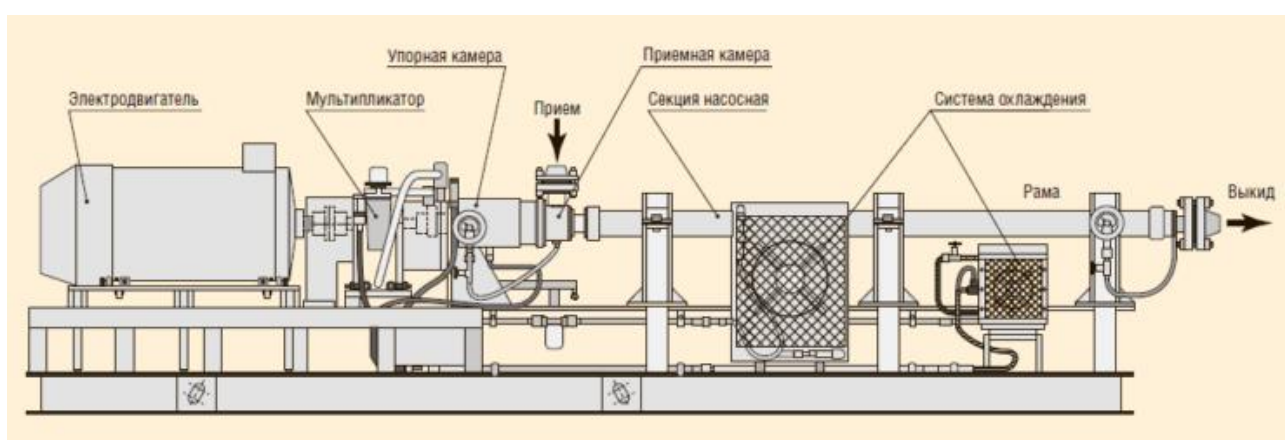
Типовая схема и типоразмеры ГНУ
